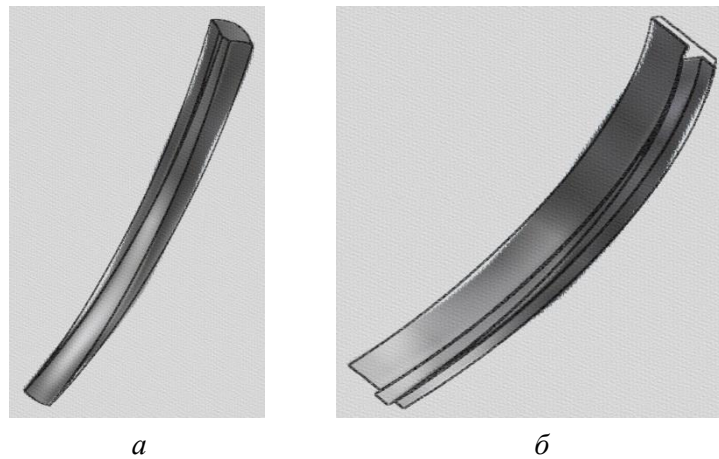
Модели стружки, получаемой при обработке фрезами с режущей кромкой типа *NR* (а) и *NF* (б)
